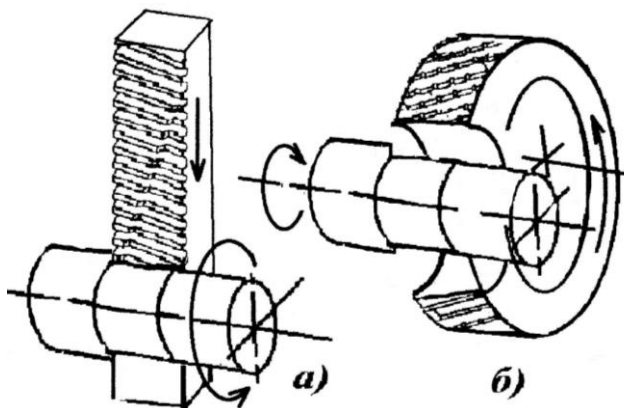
Протягивание: линейный инструмент-заготовка
